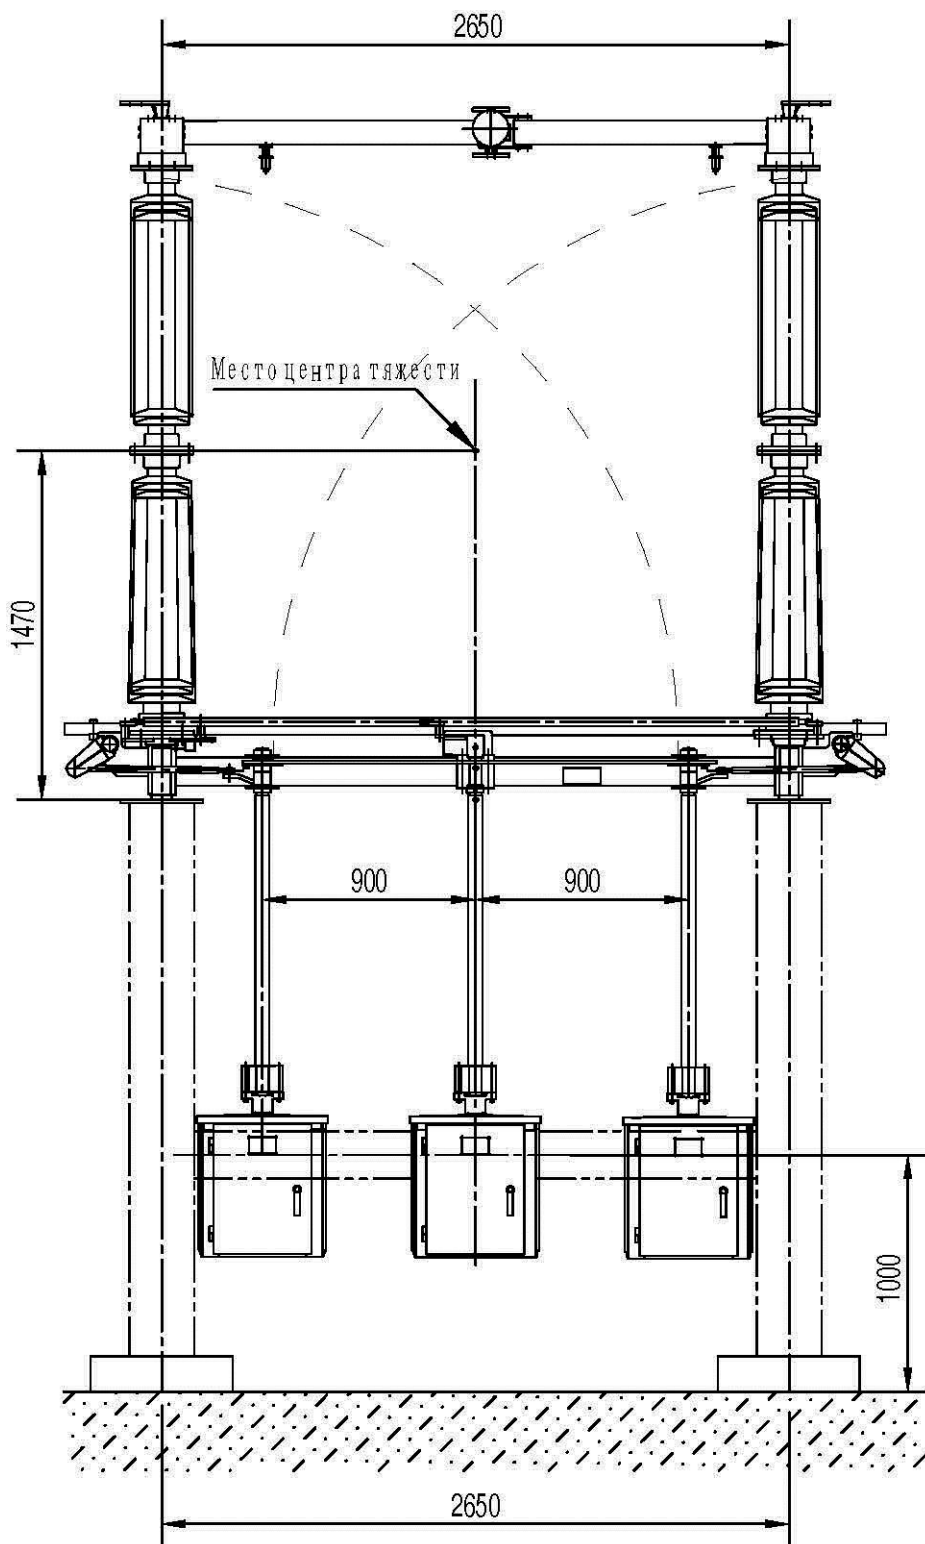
Внешний вид и габаритно-установочные размеры РГП с двигательным приводом главных и заземляющих ножей (РГП включен, пунктирной линией условно показан ход заземлителя, при открытых главных ножах)
